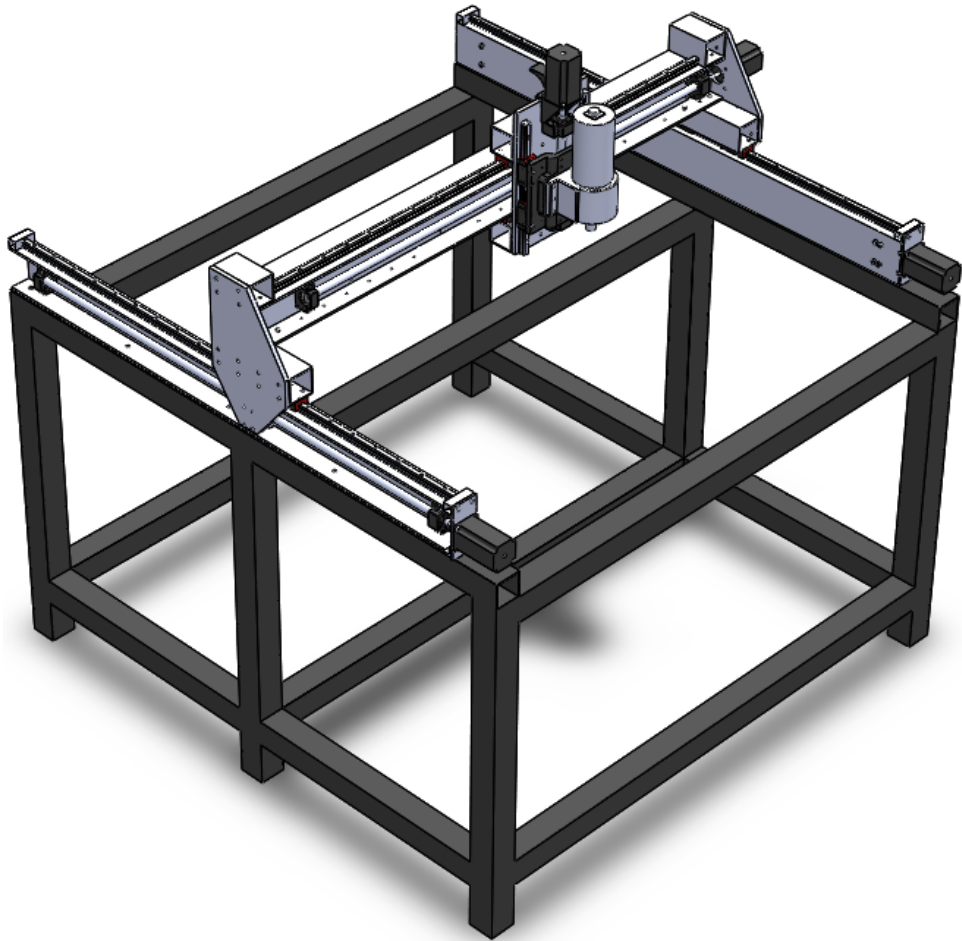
Змодельована збірка фрезерного верстату з ЧПК, вид зверху
